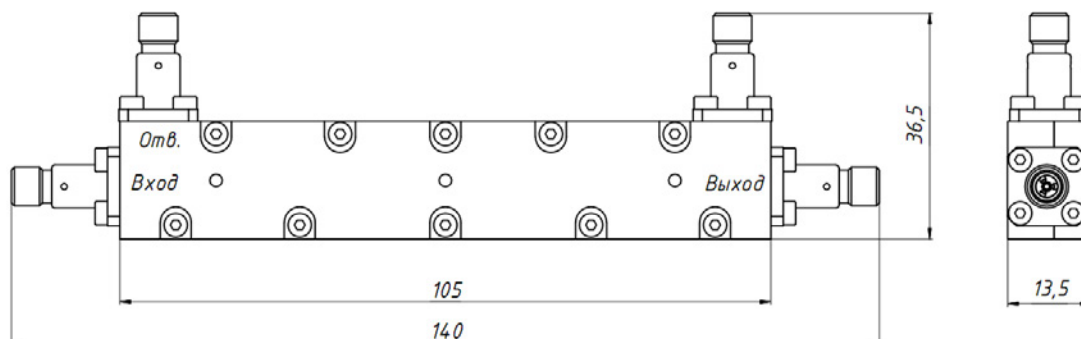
Ответвитель направленный HO16-0,5-26-03P-03P (HO16-0,5-26-13P-13P)
